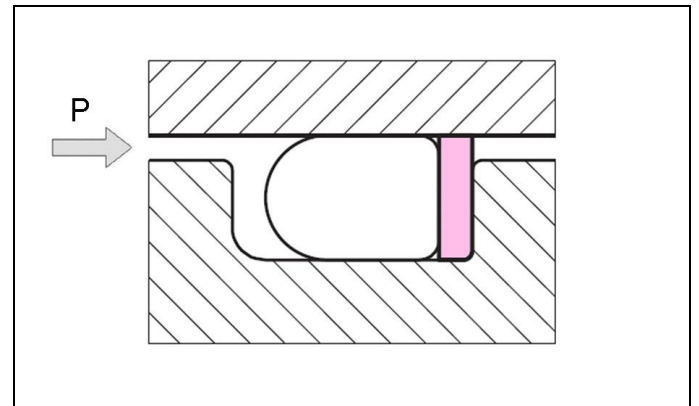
Stützring Einbau, Druckrichtung einseitig
